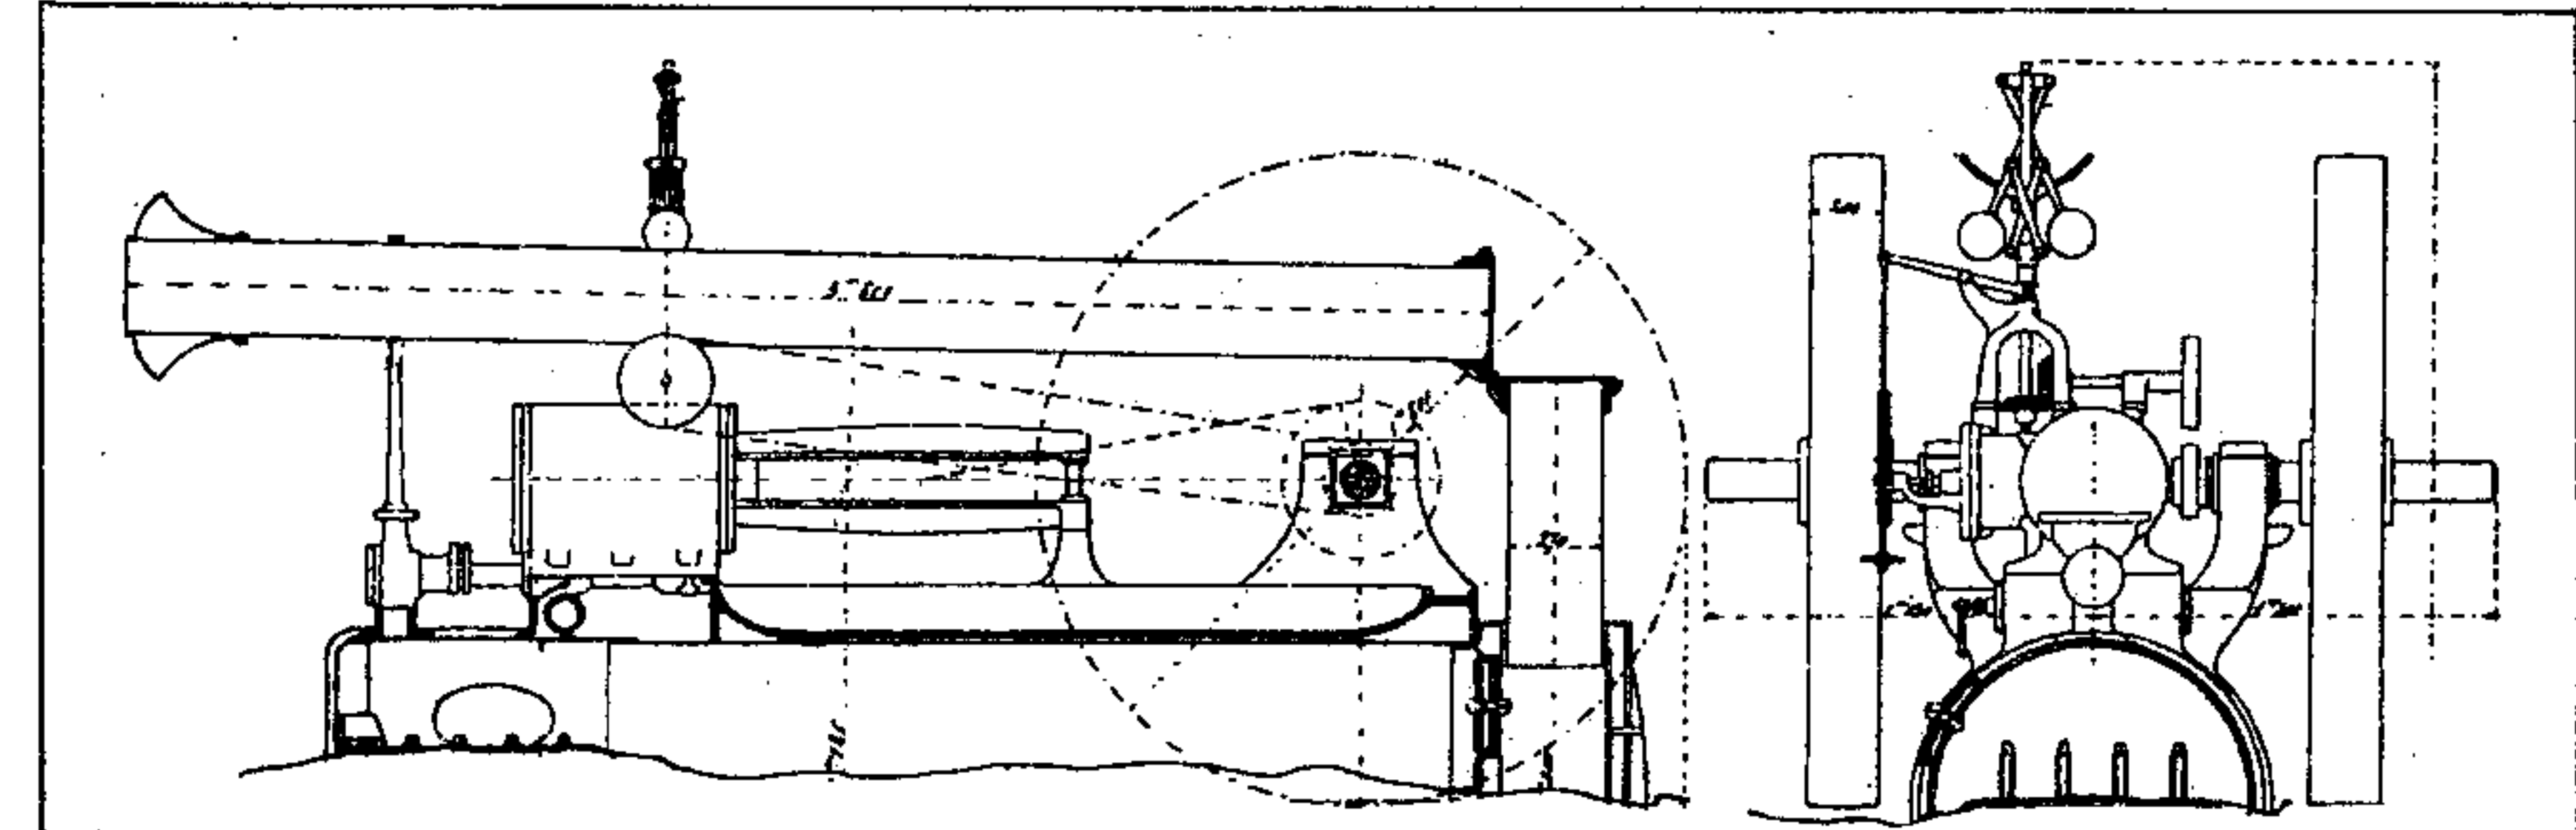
/2: Skizze der Lokomobilmaschine (1870)
